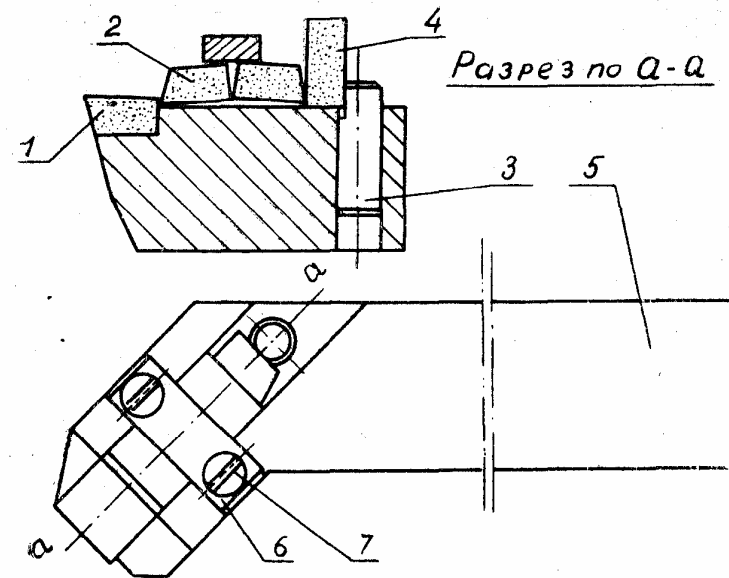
Резец с «холодным спаем». 1 — державки; 2 и 3 — пластины твердого сплава, 4 — струбцина.
